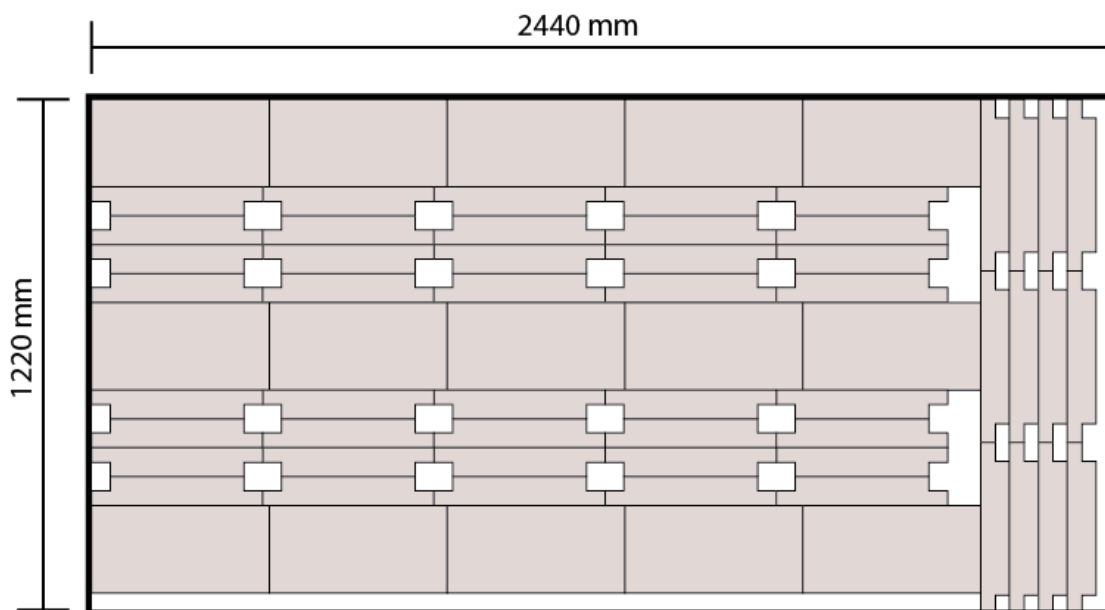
Cortes de las piezas para la “estructura de paredes de boleó” en una lámina de acero inoxidable
